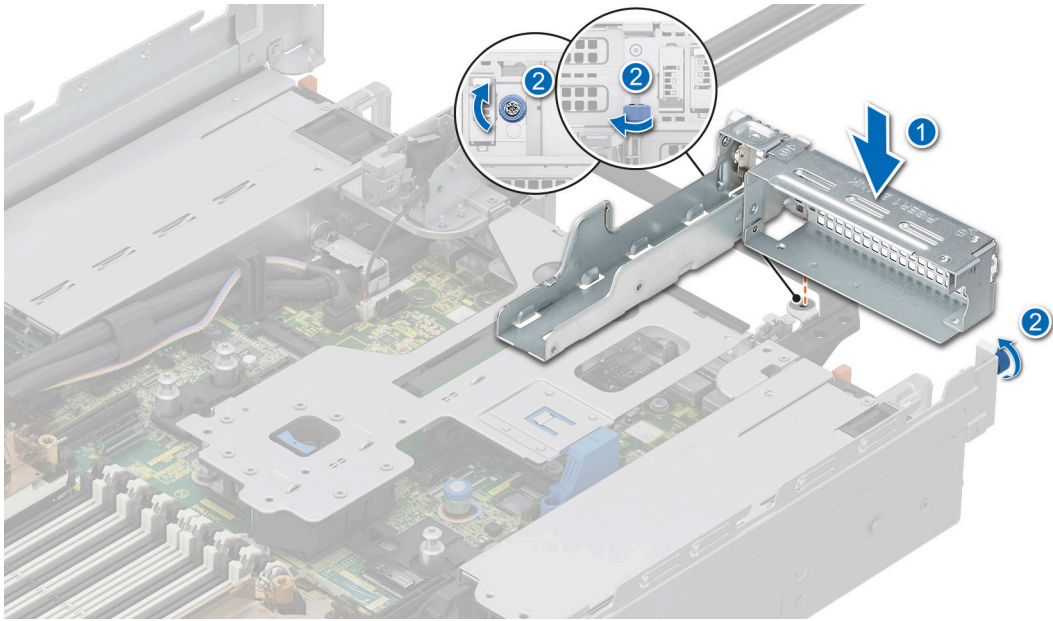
Einsetzen des Platzhalters für Riser 1
